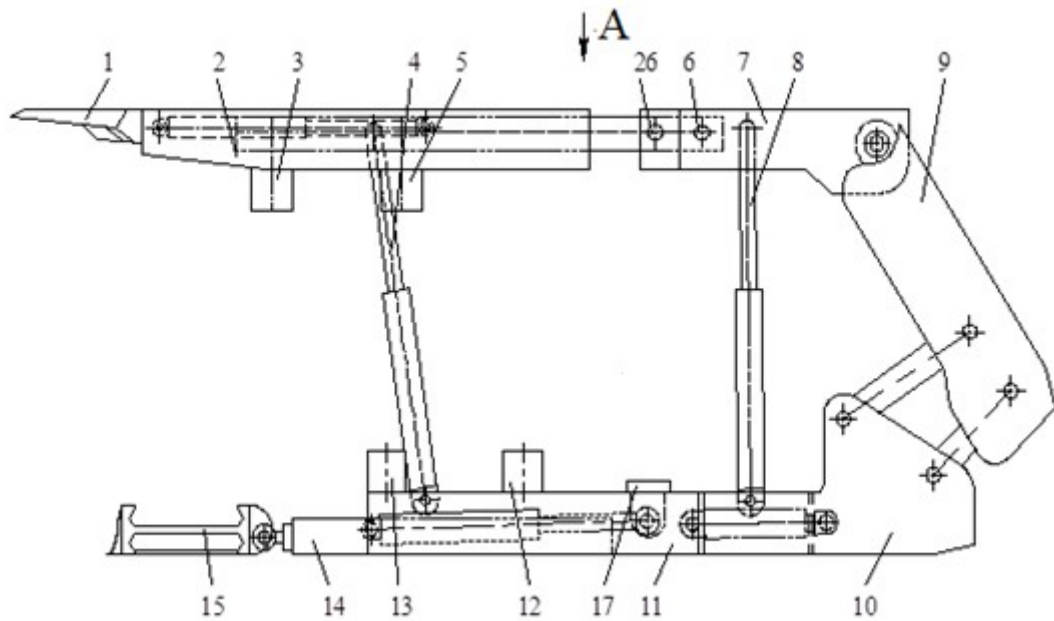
СМК с телескопическими перекрытием и основанием с выдвинутой забойной ступенью перекрытия
